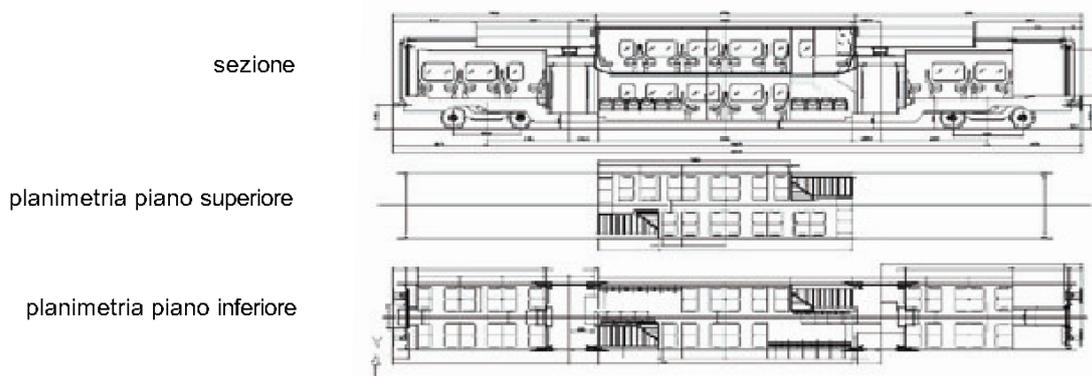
sezione e pianta delle due vetture-tipo del TSR (fonte Ansaldo Breda)
